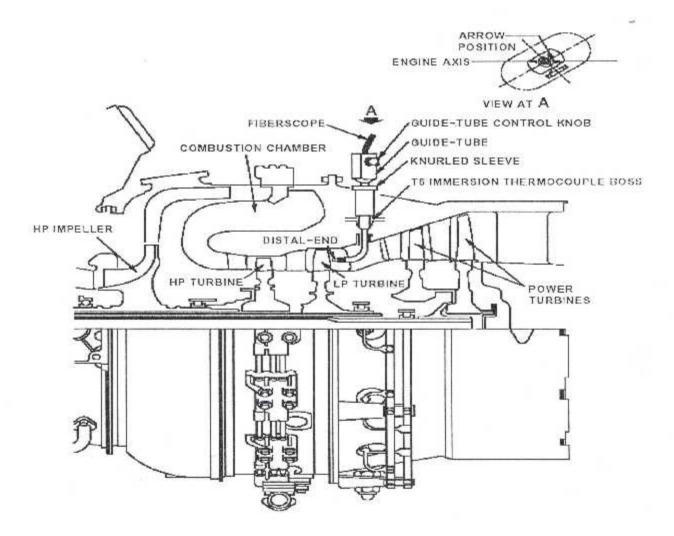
INSPECTION BOROSCOPIQUE DU STATOR ET DES AILETTES DE LA TURBINE HP
